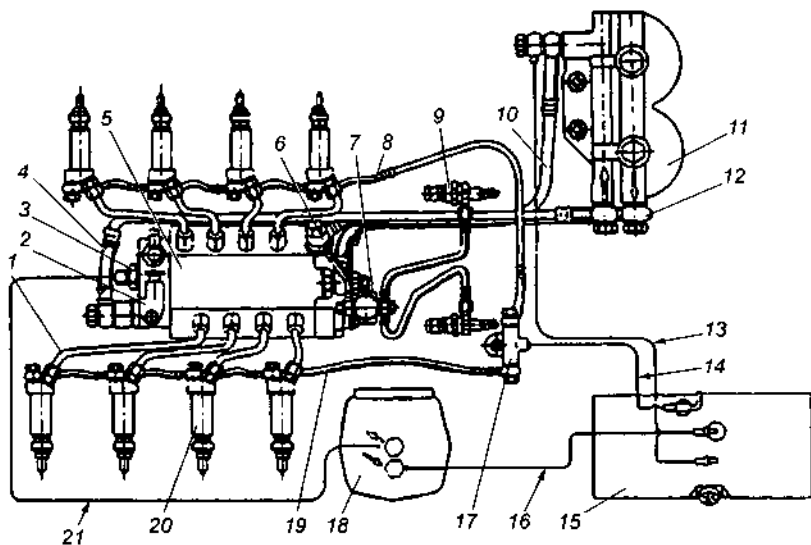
Система питания двигателя топливом: 1 — топливопровод высокого давления; 2 — ручной топливоподкачивающий насос; 3 — топливоподкачивающий насос низкого давления; 4 — топливопровод к фильтру тонкой очистки топлива; 5 — топливный насос высокого давления; 6 — топливопровод к электромагнитному клапану; 7 — электромагнитный клапан; 8 — сливной дренажный топливопровод форсунок правого ряда; 9 — свеча ЭФУ; 10 — дренажный топливопровод высокого давления; 11 — фильтр тонкой очистки топлива; 12 — подводящий топливопровод к насосу высокого давления; 13 — дренажный топливопровод фильтра тонкой очистки топлива; 14 — сливной топливопровод; 15 — топливный бак; 16 — топливопровод к фильтру грубой очистки топлива; 17 — тройник; 18 — фильтр грубой очистки топлива; 19 — сливной дренажный топливопровод форсунок левого ряда; 20 — форсунка; 21 — подводящий топливопровод к насосу низкого давления
